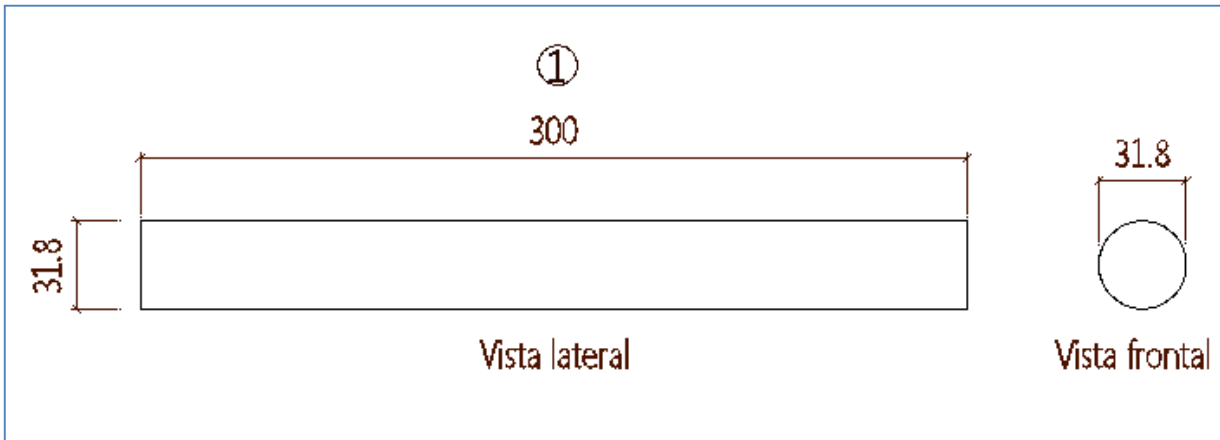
Detalle despiece pieza No.1 modelo 2 tensión.
